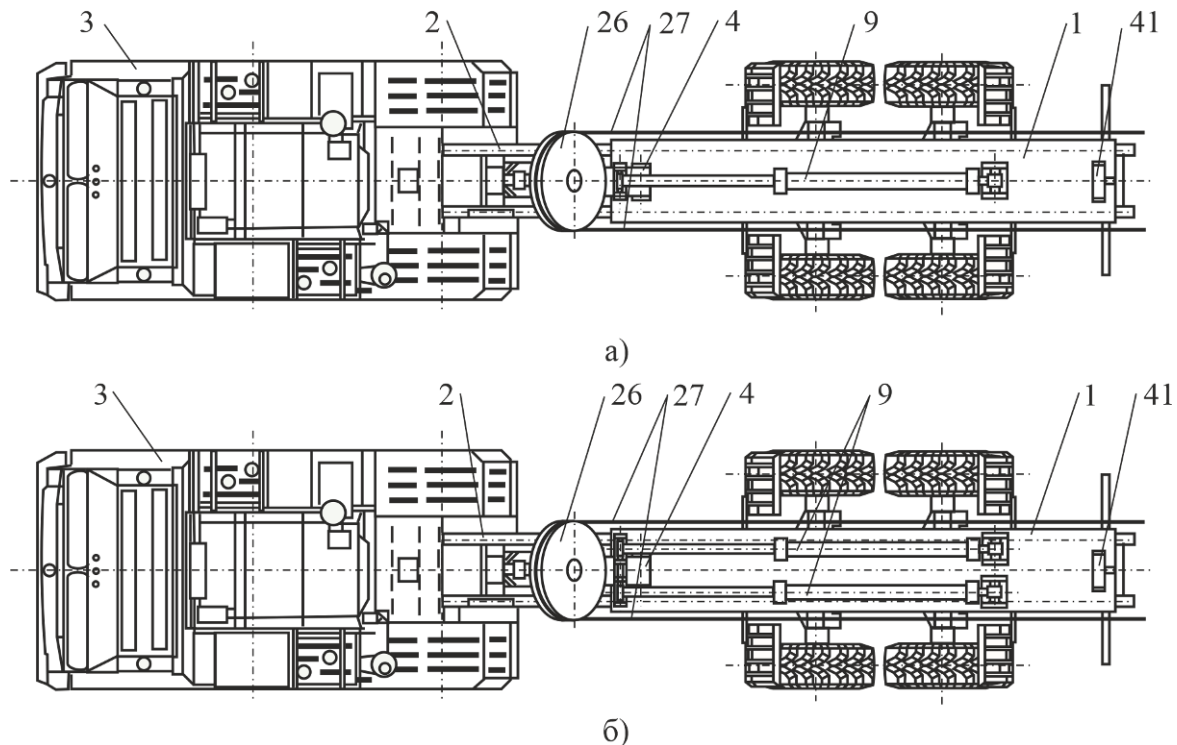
Общий вид мобильного комплекса (вид сверху) [13]: а – с одинарным подъемным гидроцилиндром; б – со сдвоенными подъемными гидроцилиндрами
